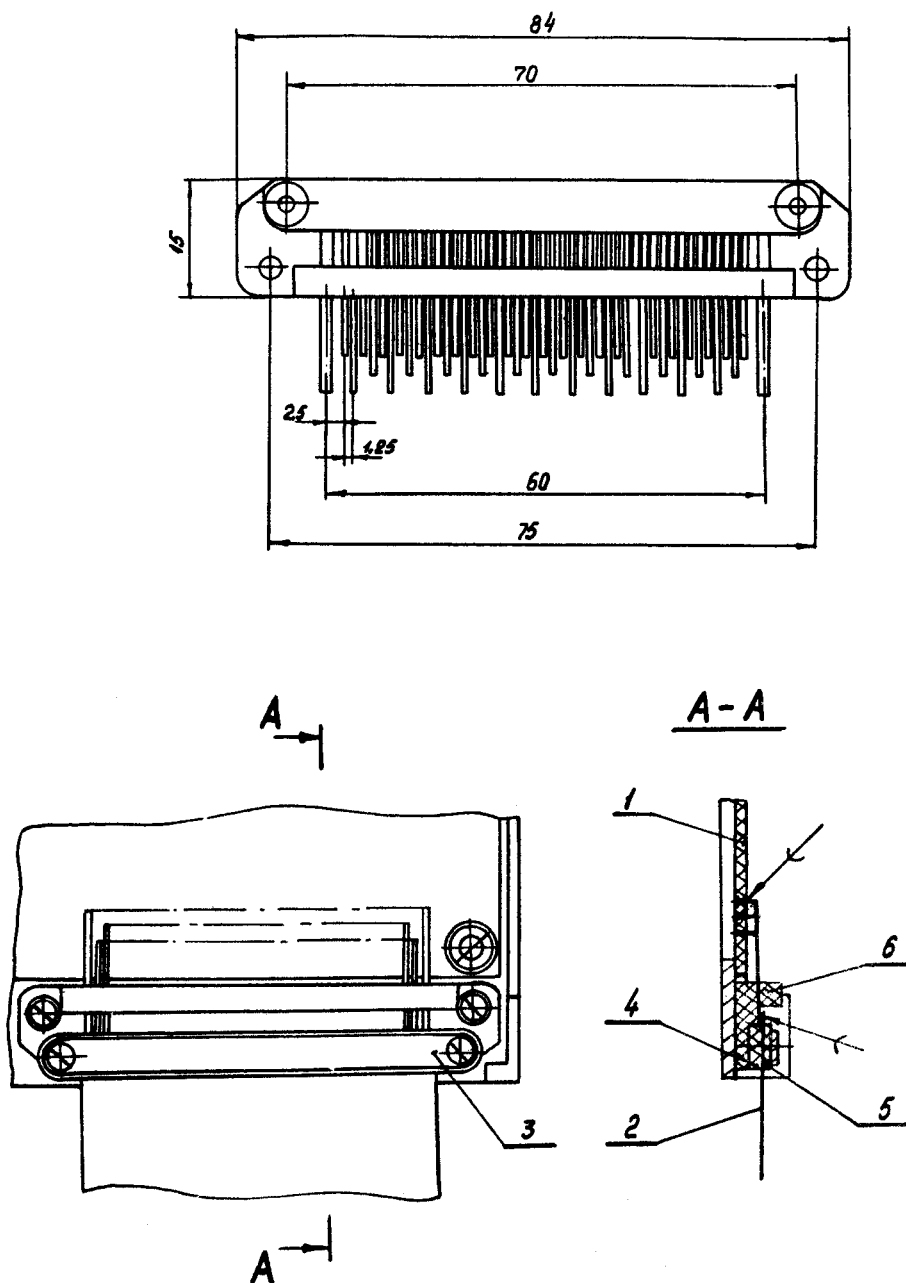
Гибкий печатный кабель с колодкой и его установка на печатную плату: 1 - плата печатная; 2 - кабель гибкий печатный; 3 - планка прижимная; 4 и 5 - прокладки; 6 – колодка
